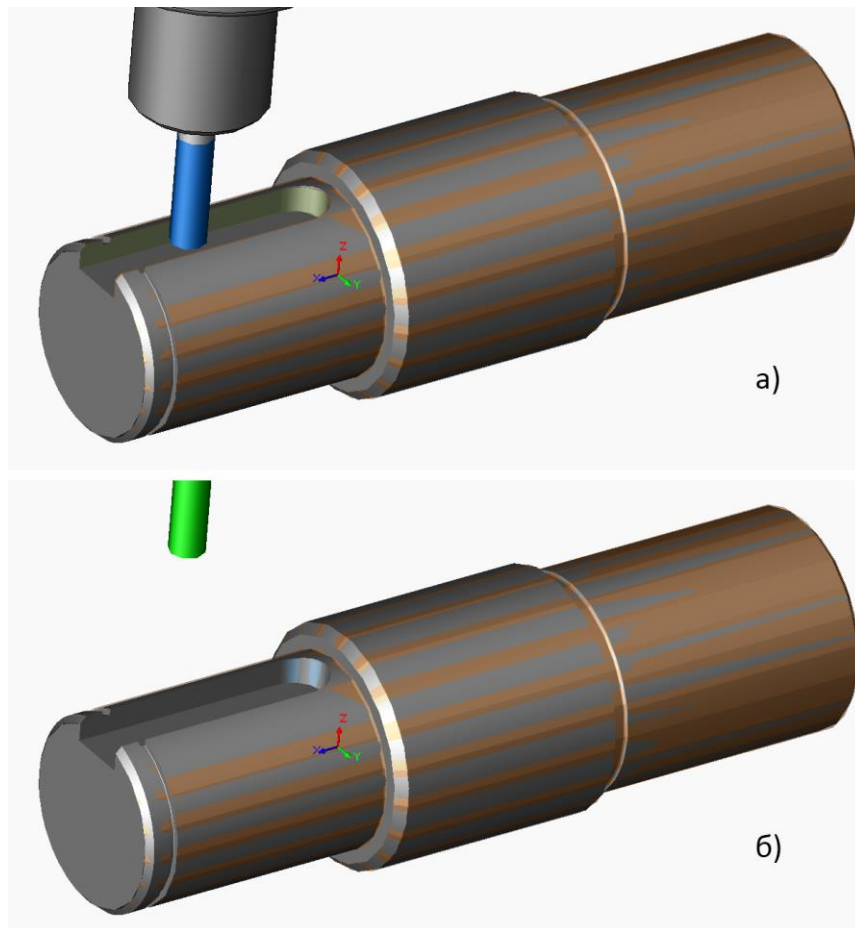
Фрагменти імітації процесу обробки деталі: а) чорнове фрезерування; б) контурне фрезерування.
